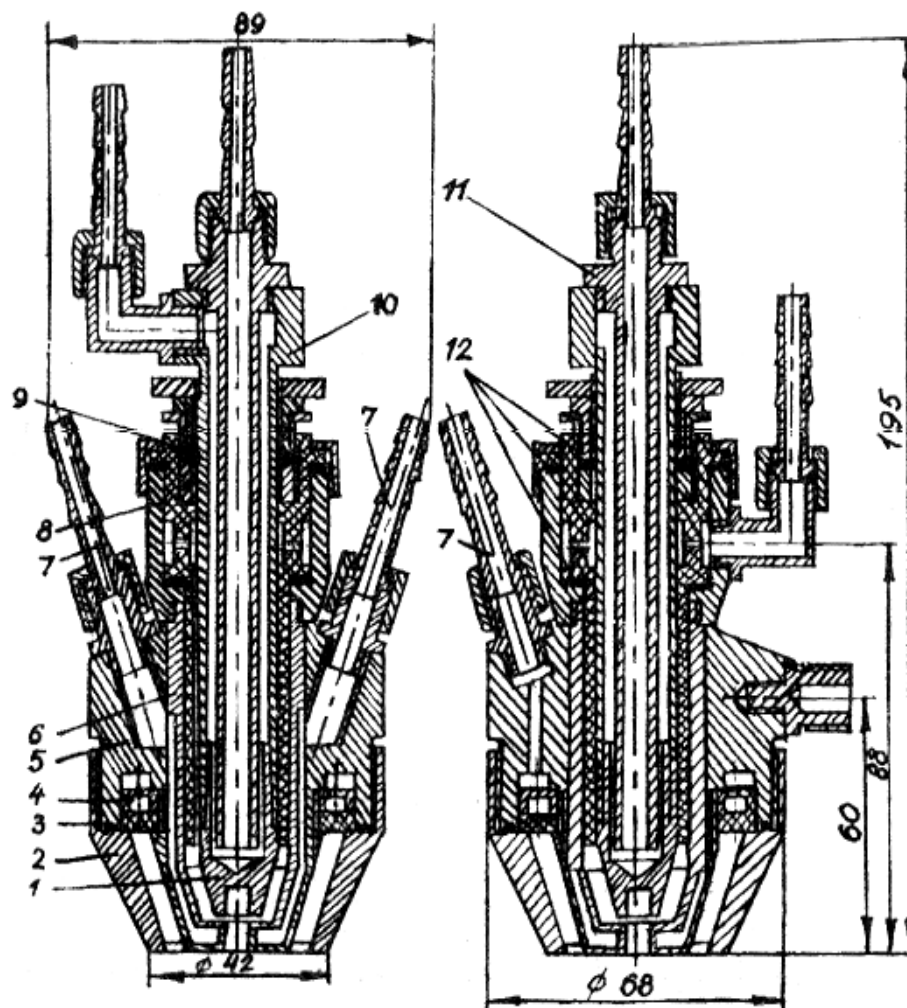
Общий вид установки плазменной наплавки порошковыми проволоками УД-417
